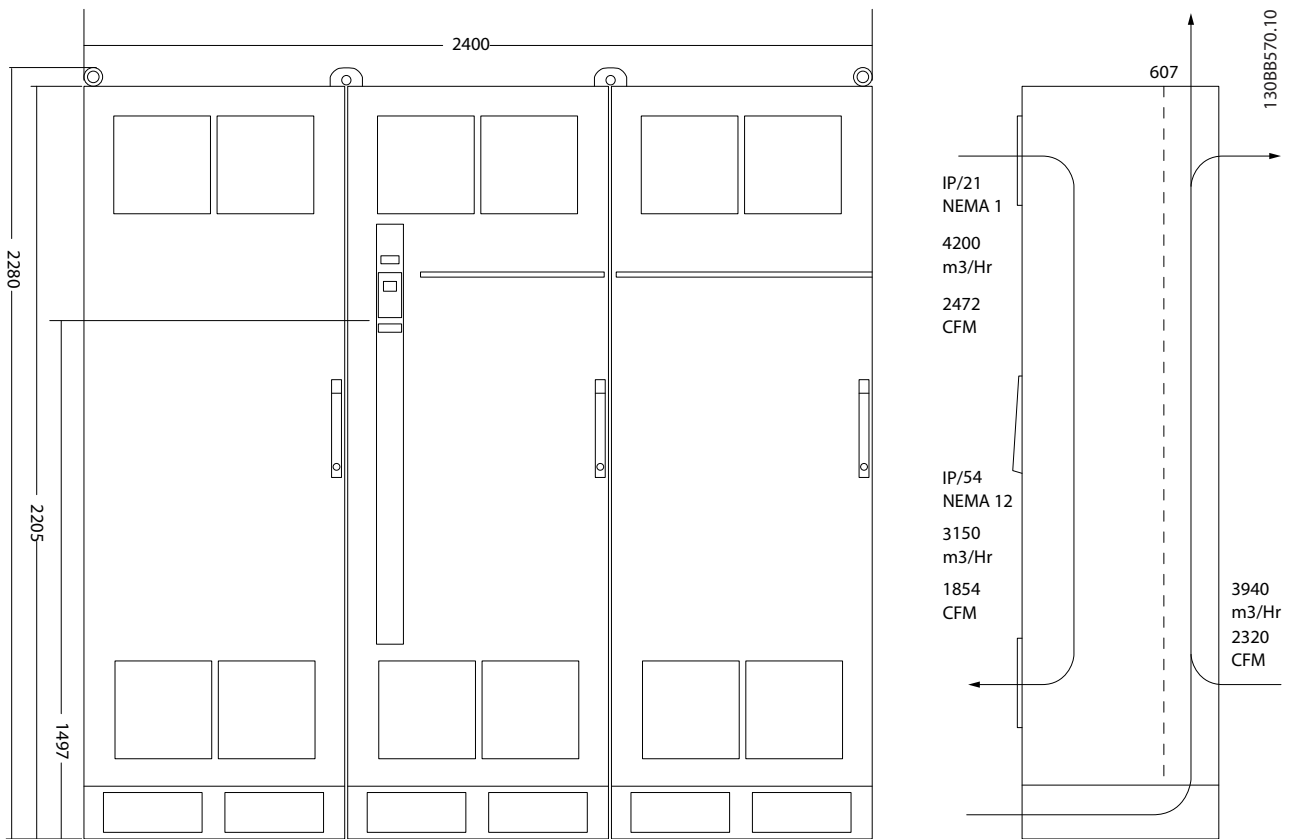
Mechanische afmetingen (mm), F9
